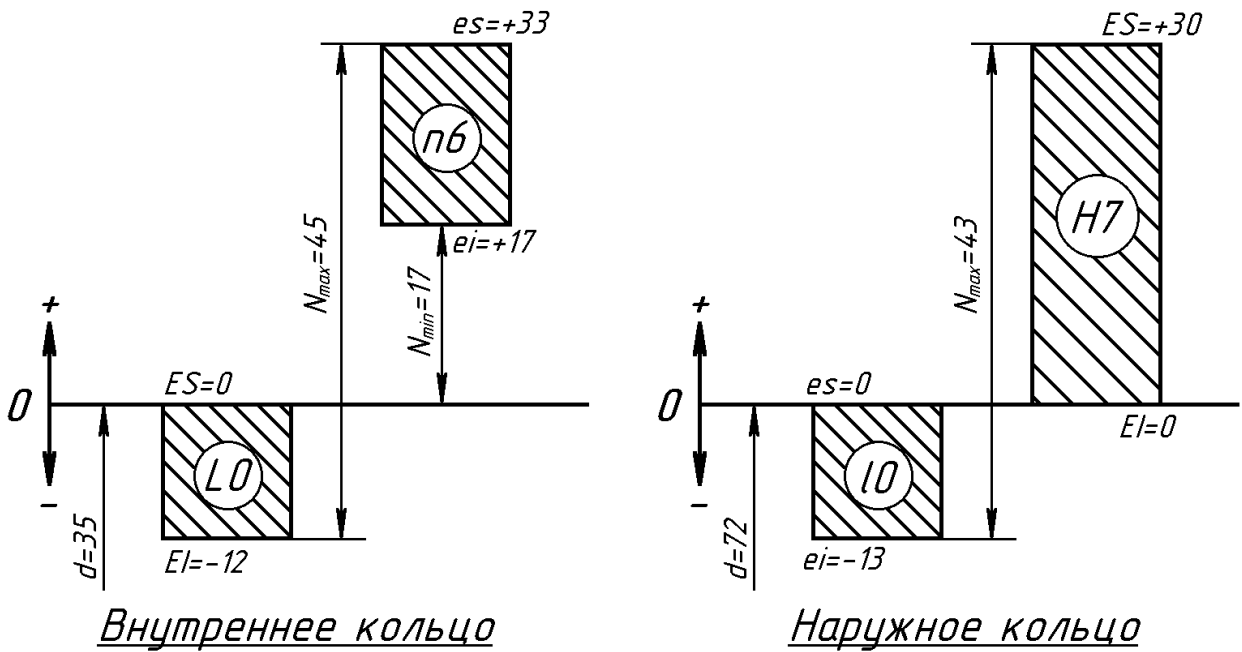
Схемы расположения полей допусков колец подшипников качения
